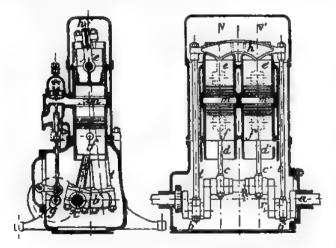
u. 13. Zweicylindriger Motor System Gobron & Brillié,
